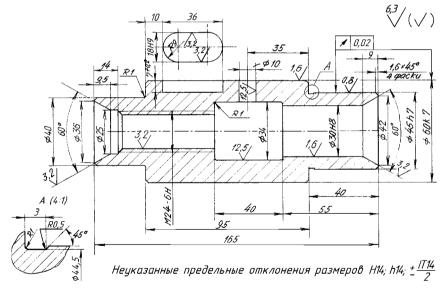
Чертеж детали с конструкторско-технологическим кодом 401594.87302.312302A
